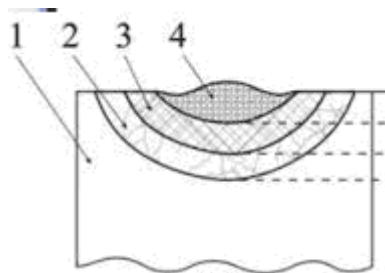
Схема формування шарів в зоні лазерного впливу під час обробки з оплавленням поверхні.
